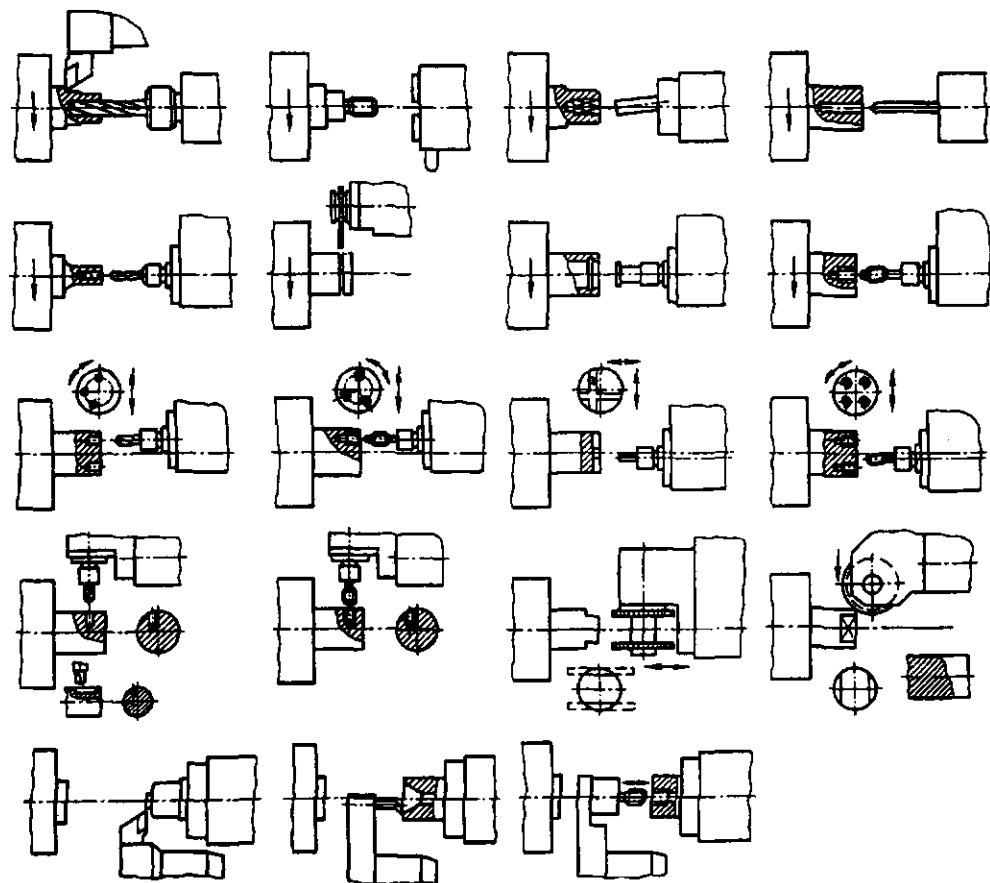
Схемы обработки поверхностей деталей на токарных станках с ЧПУ с использованием специальных инструментальных шпинделей
